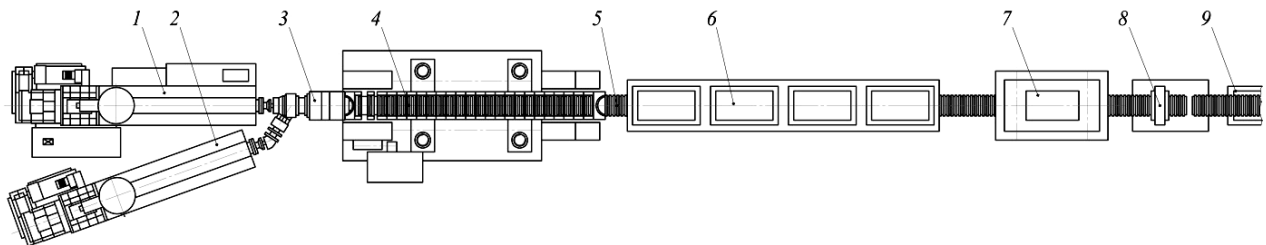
Принципова апаратно-технологічна схема виробництва двошарових полімерних гофрованих труб: 1, 2 – екструдери; 3 – трубна головка; 4 – гофратор; 5 – полімерна гофрована труба; 6 – ванна охолодження; 7 – тягнучий пристрій; 8 – відрізний пристрій; 9 – приймальний пристрій
